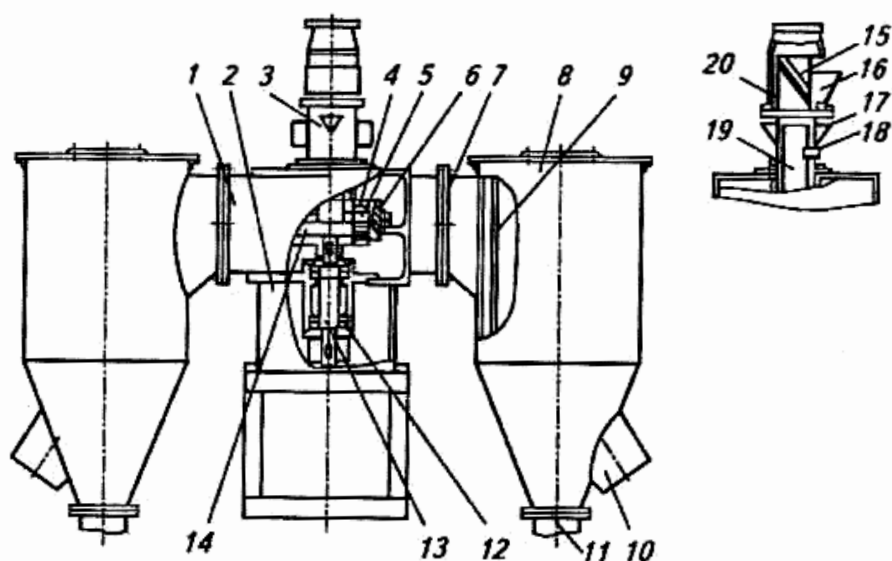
Центробежная обрубивающая машина А1-МЦП: 1 — корпус; 2 — станина; 3 — распределительное устройство; 4 — рабочие диски; 5 — направляющие каналы; 6 — кольцевая дека; 7 — тангенциальные патрубки; 8 — циклон; 9 — цилиндрическое сито; 10 — отводящая течка для рушанки; 11 — отводящая течка для масличной пыли; 12 — подшипники; 13 — вертикальный вал; 14 — кольцевая перегородка; 15 — предохранительная решетка; 16, 17 — карманы; 18 — трубка для всасывания воздуха; 19 — цилиндрический патрубок; 20 — цилиндрическая камера
